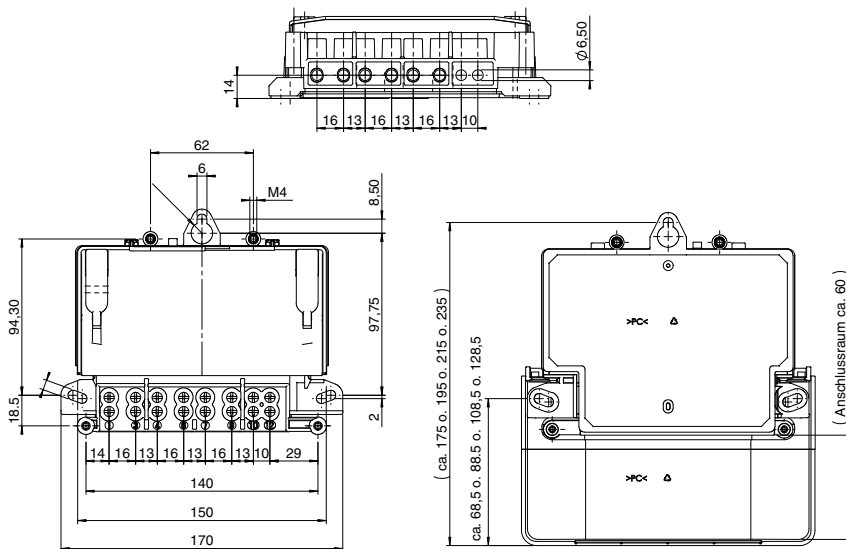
Maßblatt Q3D x1xxx (60-Ampere-Ausführung mit Klemmendurchmesser 6,5 mm)
